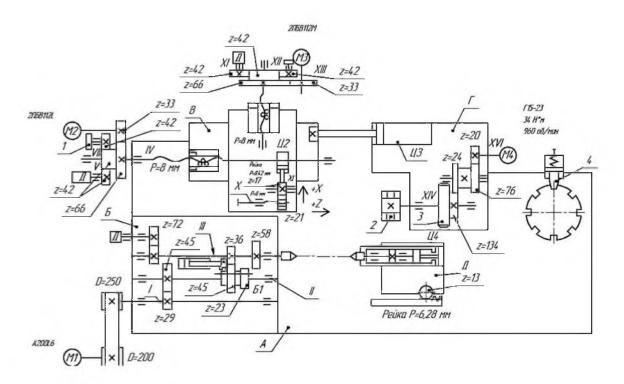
Кинематическая схема станка с ЧПУ 1725МФ3
